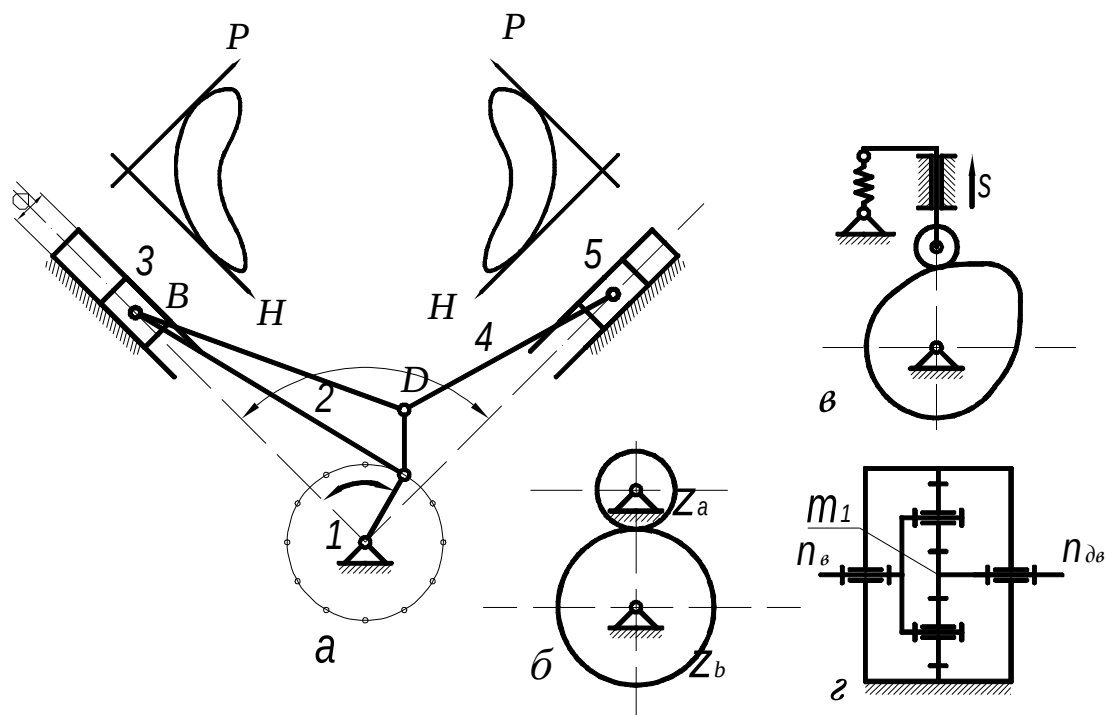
На схеме: а- рычажный механизм компрессора; б- открытая зубчатая передача; в- кулачковый механизм; г- привод рычажного механизма
